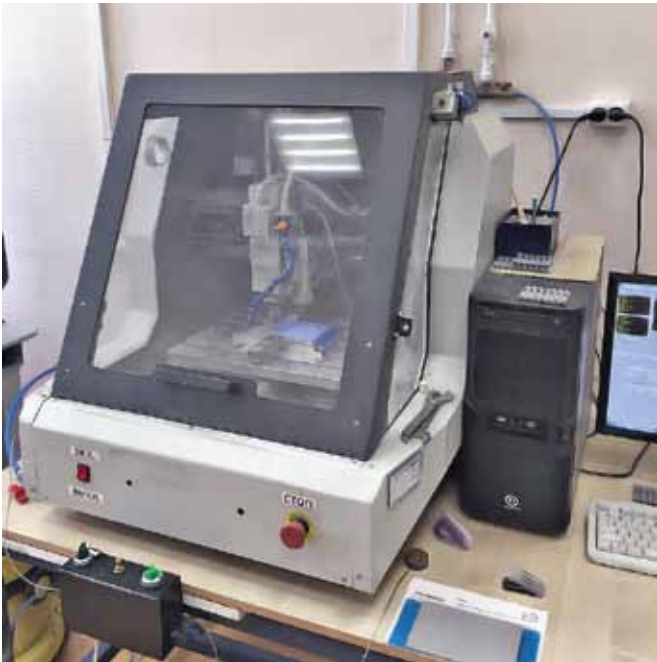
Фрезерный станок с ЧПУ «Роутер 4030РС»
